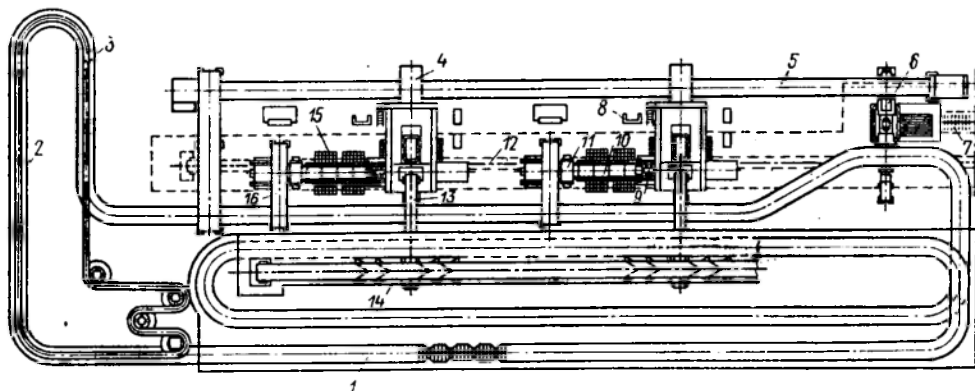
Формовочная линия с двумя автоматами 8L91265СМ:
